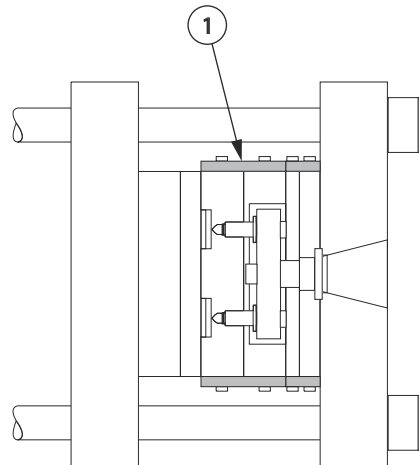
Arretieren der Kavitätenplatte am Heißkanal (Draufsicht)
